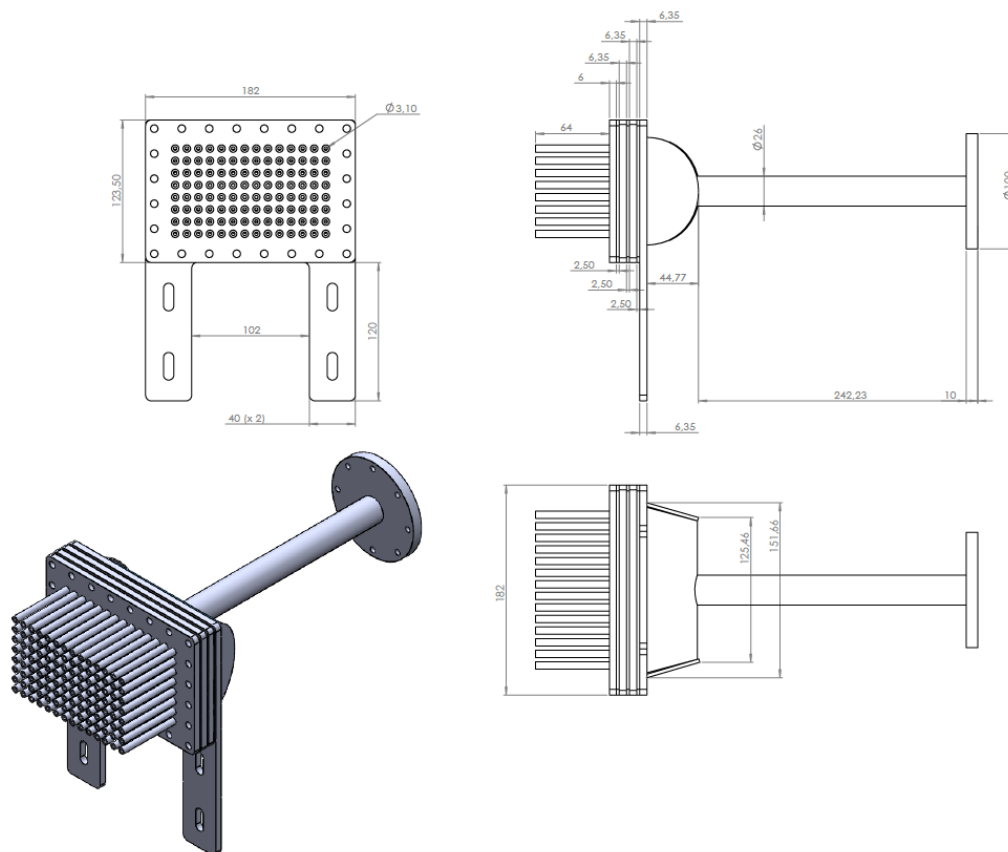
Desenho técnico da primeira placa furada do retificador.
